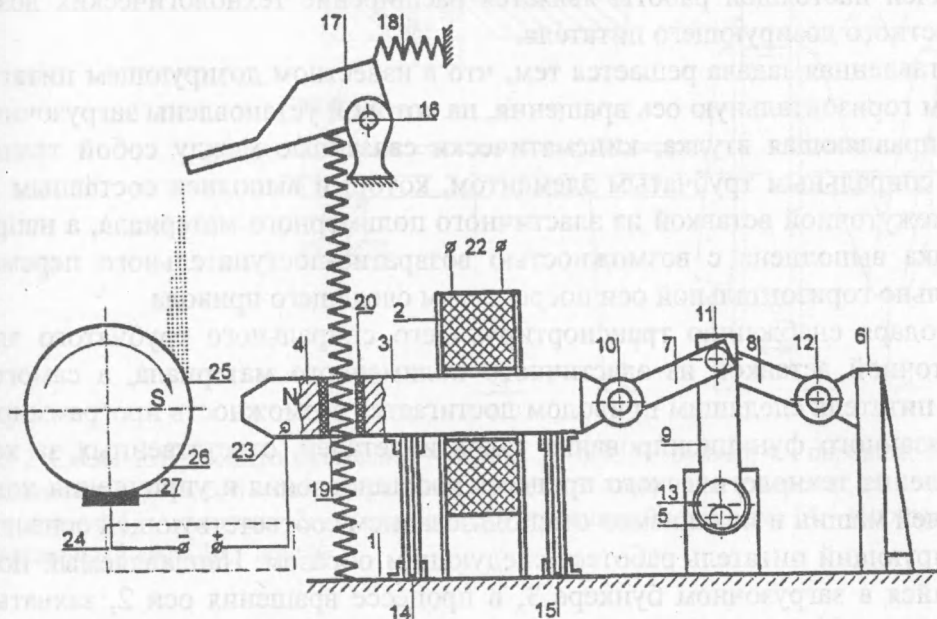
Схема устройства для электромагнитной наплавки: 1 – электрически изолированное основание; 2 – катушка; 3 – сердечник; 4 – полюсный наконечник; 5 – выходной вал двигателя; 6, 7, 8 – рычаги; 10, 11, 12 – шарниры; 13 – эксцентрик; 14, 15, 16 – опоры; 17 – дозирующее приспособление; 18 – пружина; 19 – вертикальное отверстие; 20 – диэлектрическая втулка; 21 – линейный упругий элемент; 22, 23 – контакты; 24 – источник разрядного тока; 25 – поверхность детали; 26 – деталь; 27 – скользящий контакт
